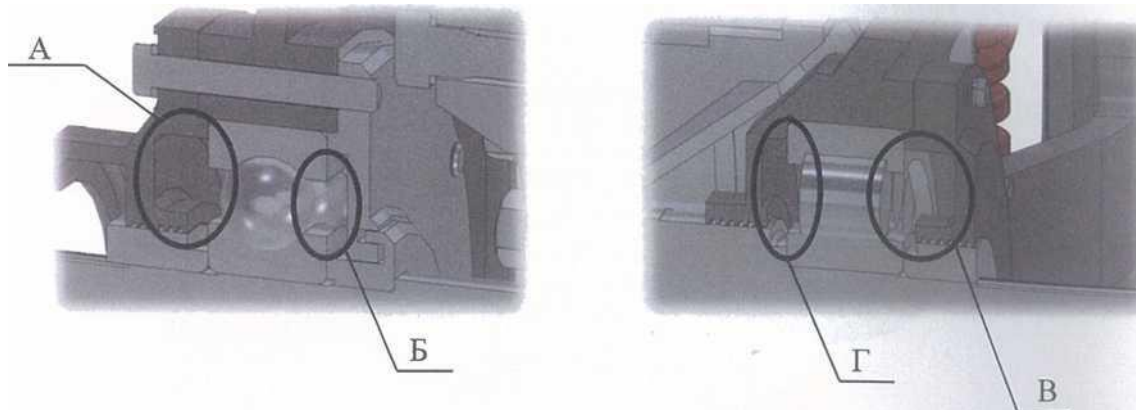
Пополнение смазки в подшипниковых узлах
